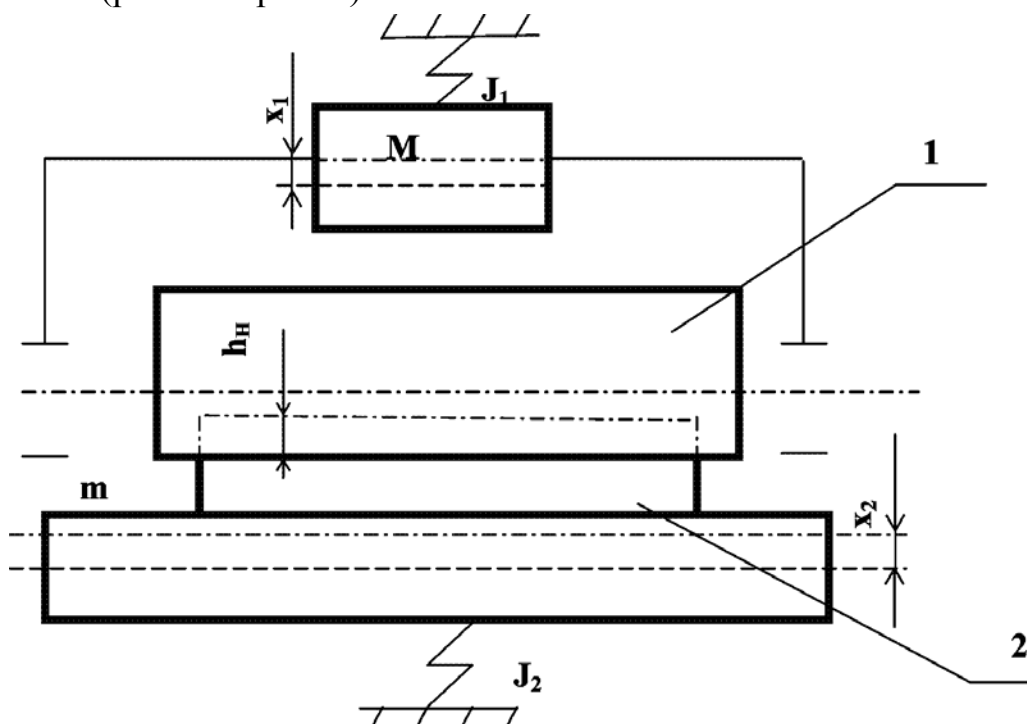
Розрахункова схема динамічної моделі процесу однобічного калібрування-шліфування: 1 – шліфувальний інструмент; 2 – оброблювана заготовка
